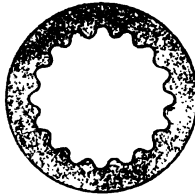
Zugsconstruction von 16 Zügen mit rundem Profil.
